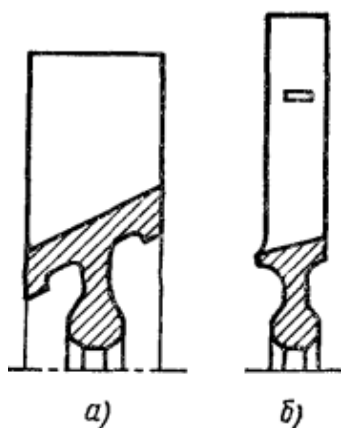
Схема широких лопаток и лопаток с бандажными полками
